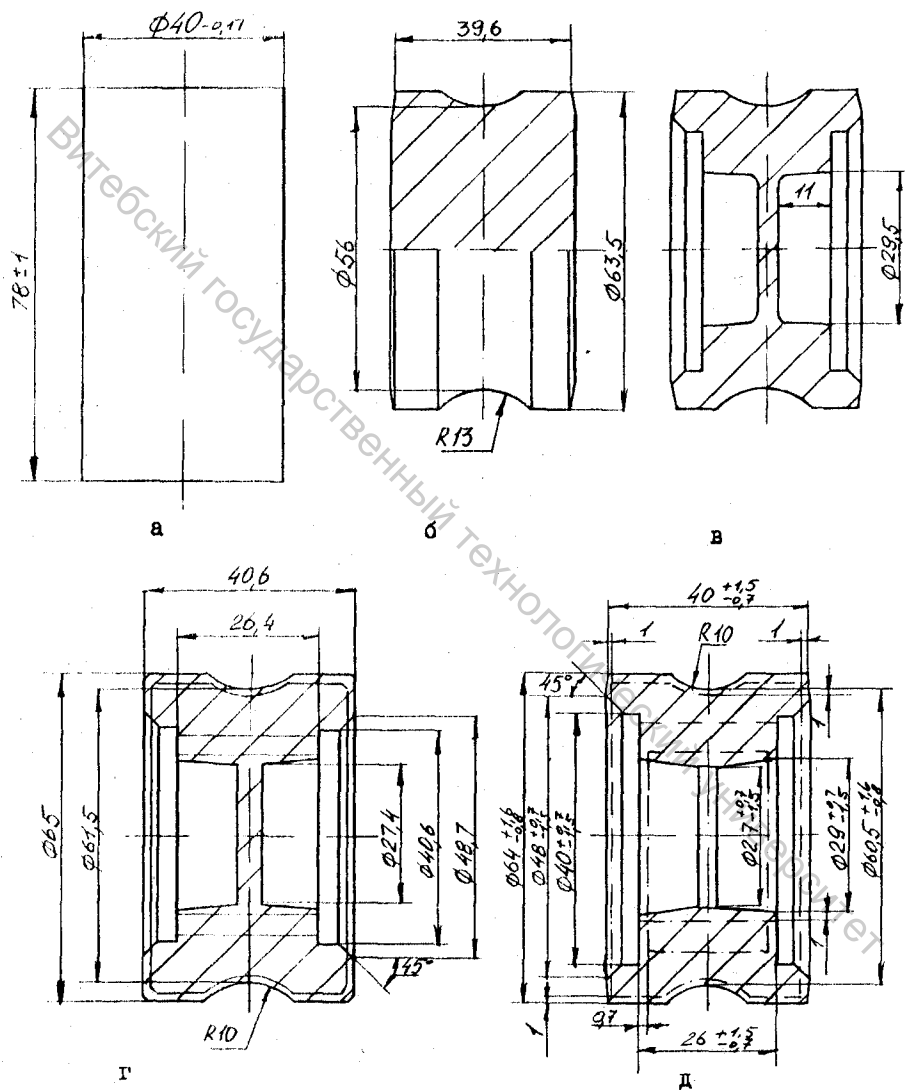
Переходы штамповки и чертеж поковки шестерни
